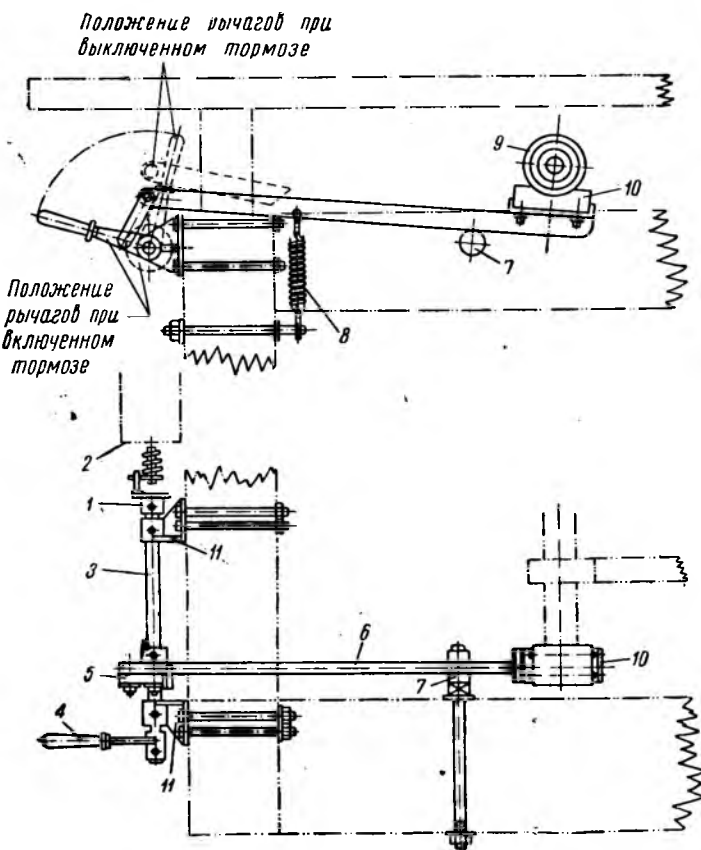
Схема рычажного тормозного приспособления к круглопильным станкам, заблокированного с рубильником
